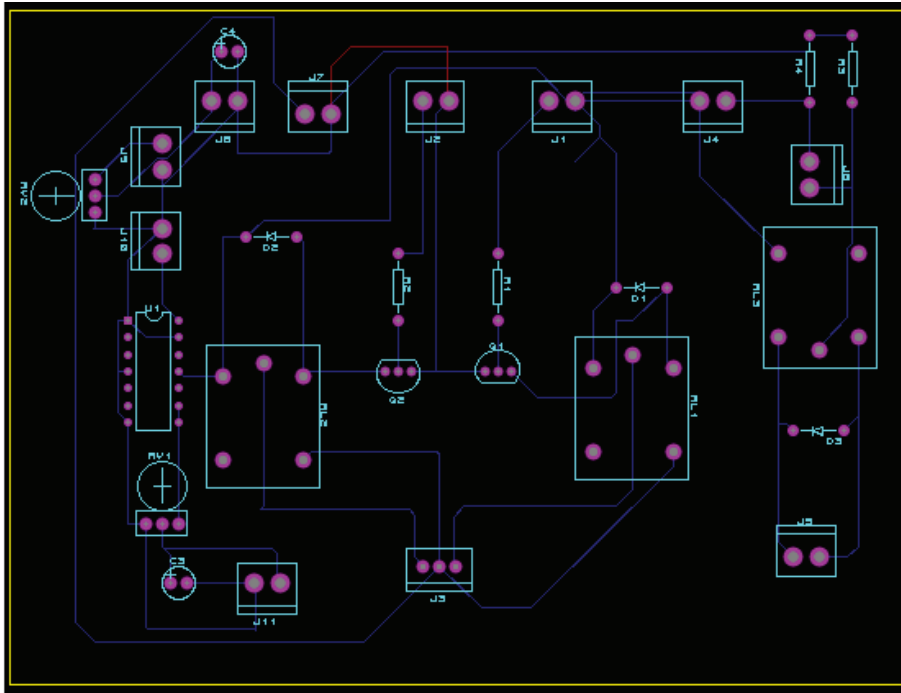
Esquema del circuito de control para PCB diseñado en Proteus.
